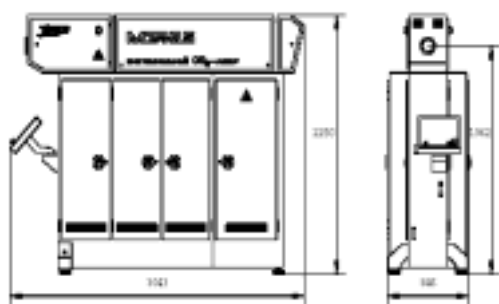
Общий вид и размеры лазера МТЛ-2.5.
